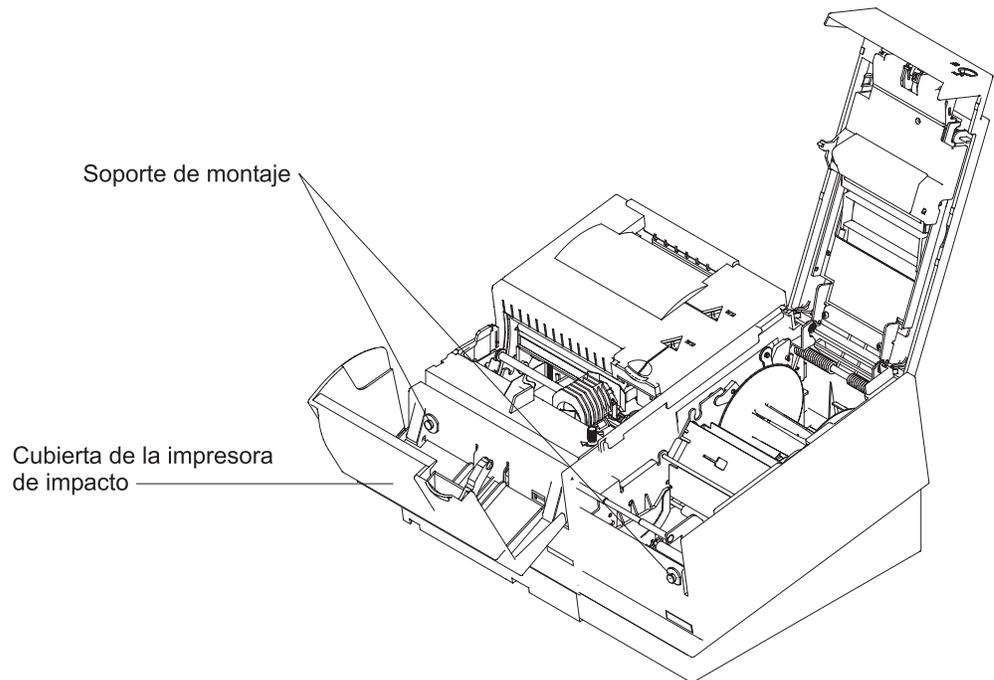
Soportes de montaje en el lado frontal de la cubierta
